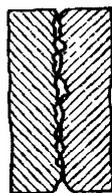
Схема контактных поверхностей свариваемых деталей
